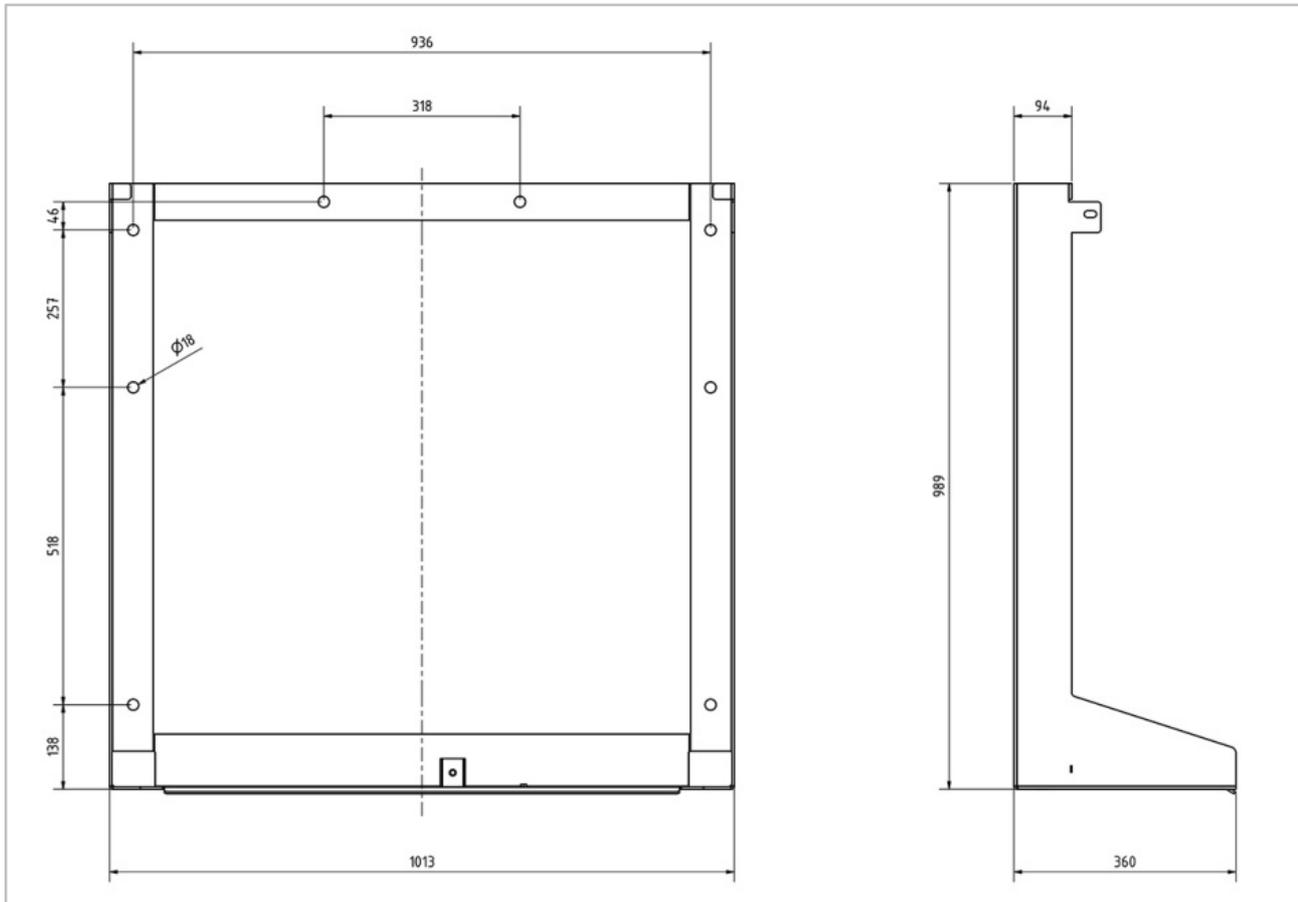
Abmessungen Wandhalter (Maße in mm)
